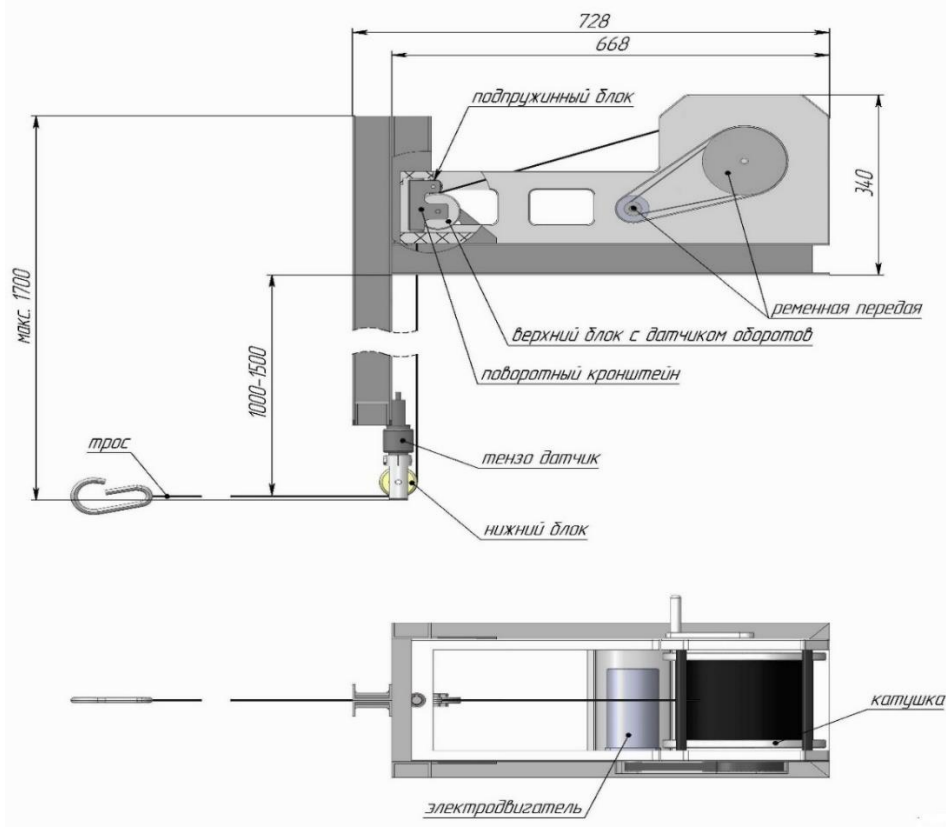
Тензометрический стенд (вид сбоку и сверху)
